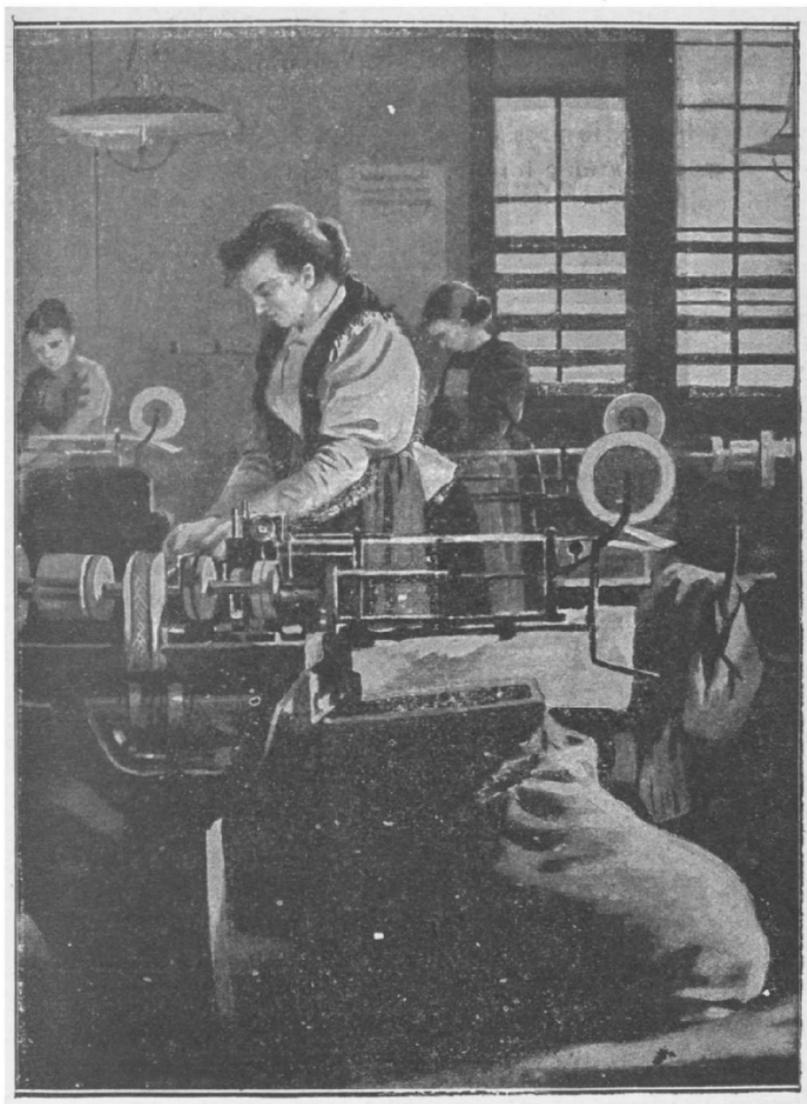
Machine Découfê, à faire les cigarettes bourrées
